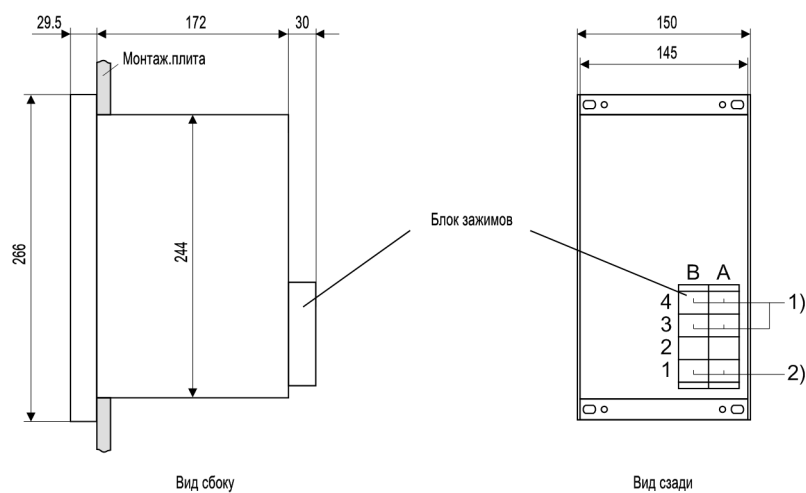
Размерные эскизы варианта устройства 7UM622 для навесного монтажа на панели (размер корпуса 1/1)
